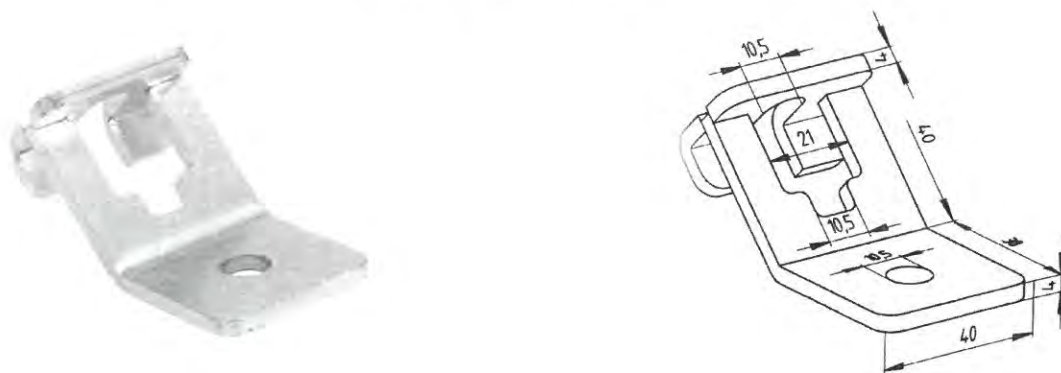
Formă și dimensiuni placă de ancorare FSB 45°
